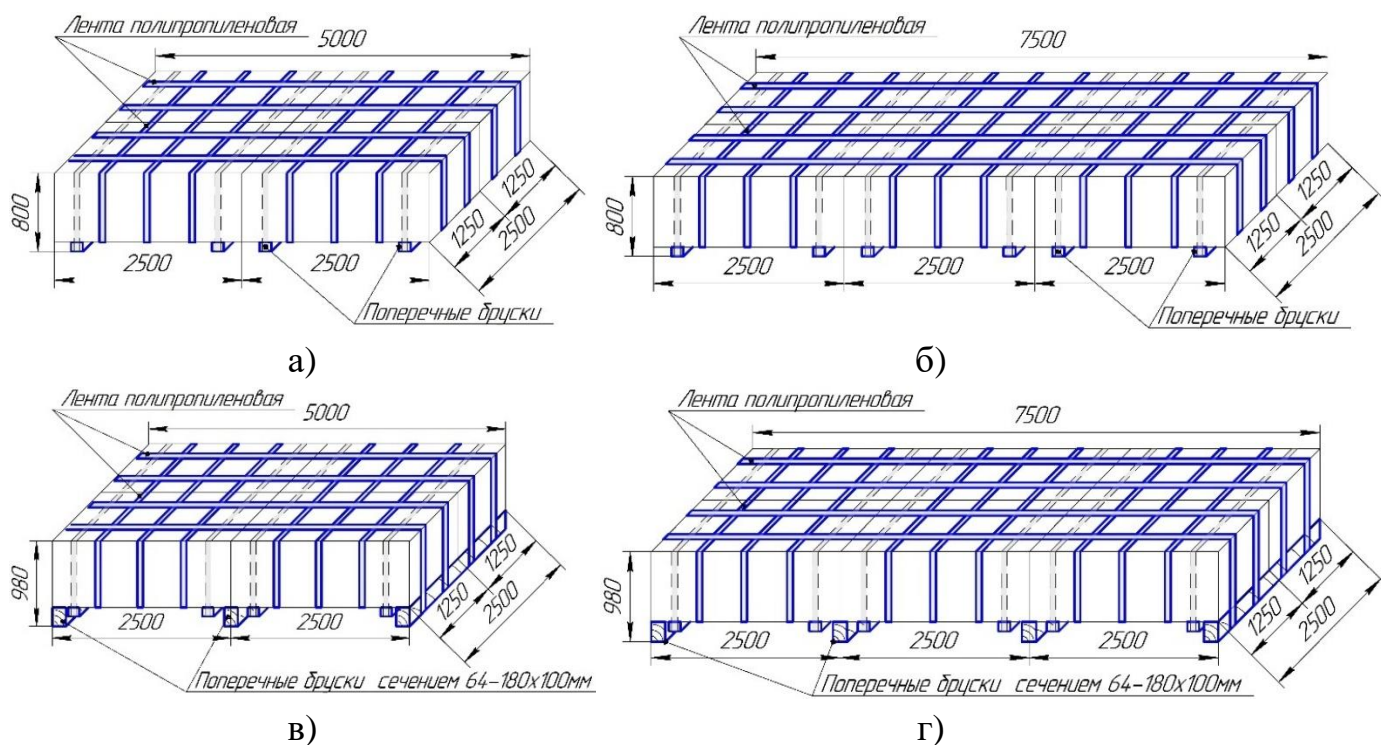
Вид транспортного пакета плит размером 5000-7500x2500мм
